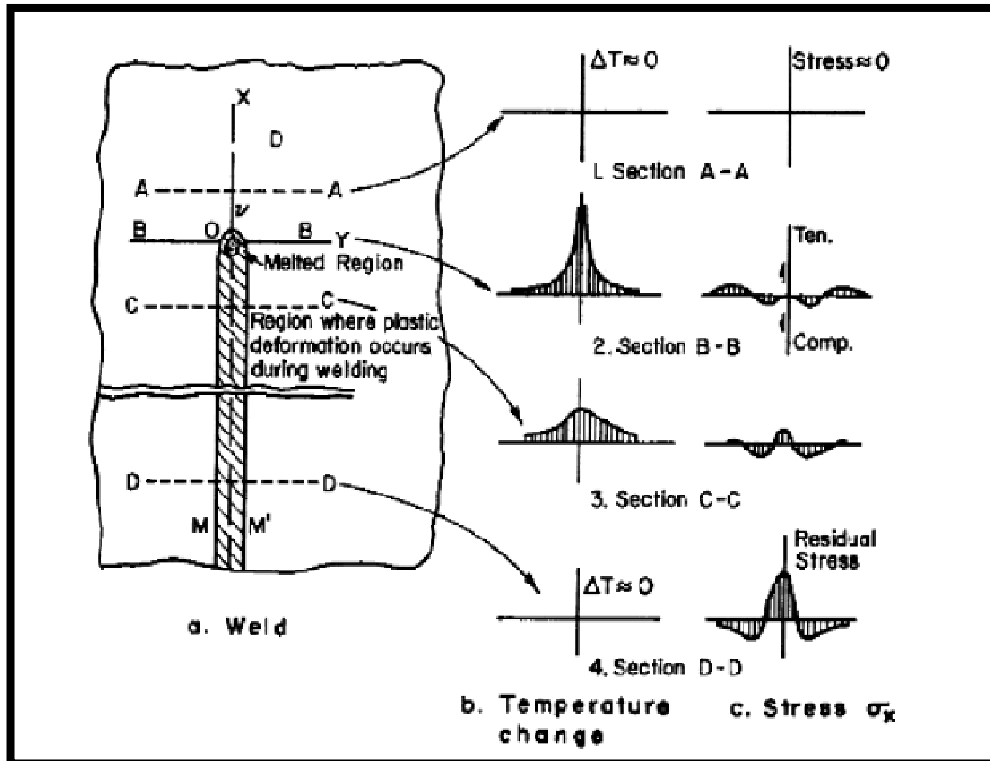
Aplicación de soldadura a lo largo de una placa. [8]
